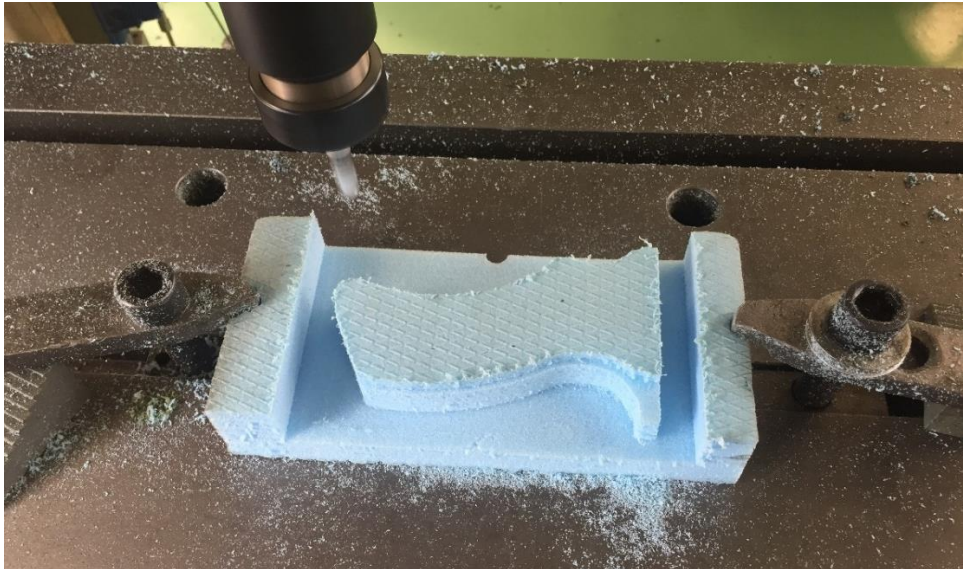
Stegnuti pripremak na radnom stolu glodalice
